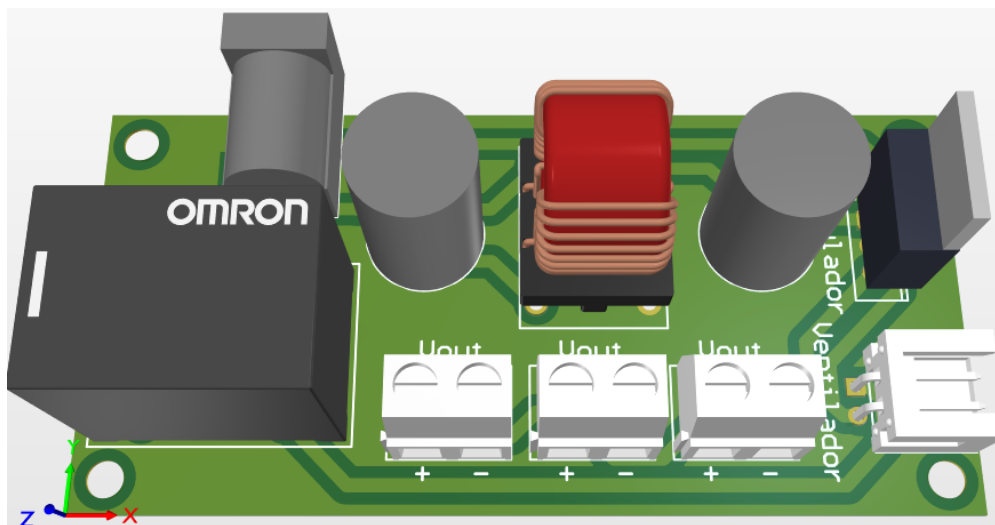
Vista 3D del diseño de PCB de la fuente de alimentación
